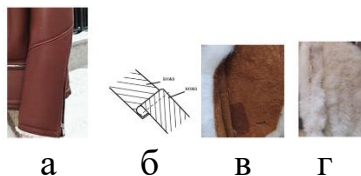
Настрочной шов с открытыми срезами: а) внешний вид соединения в готовом изделии; б) схема соединения; в) экспериментальный образец соединения деталей двухсторонней овчины со стороны кожной ткани; г) экспериментальный образец соединения деталей двухсторонней овчины со стороны волосяного покрова
